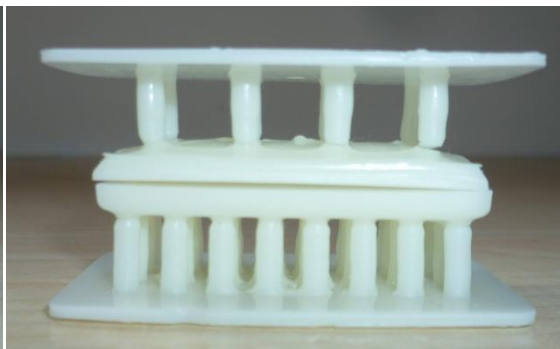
Pieza probeta 4 sobre pieza probeta 1
